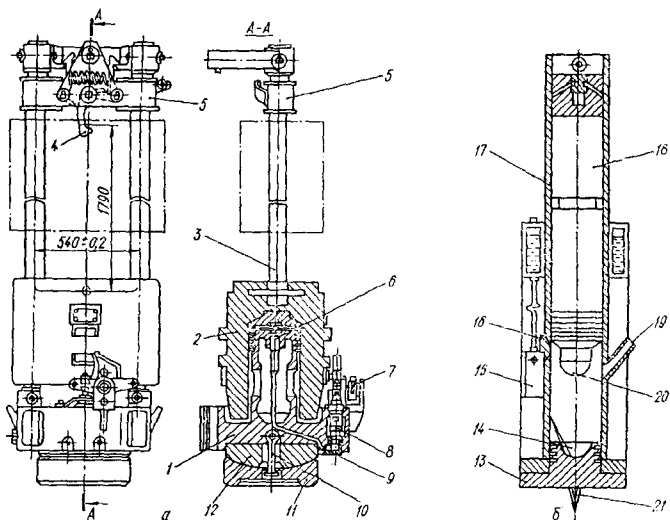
Дизельные молоты: а – штанговый; б – трубчатый; 1 – поршень; 2 – цилиндр; 3 – штанга; 4 – крюк; 5 – кошка; 6 – форсунка; 7 – толкатель; 8, 15 – топливные насосы; 9 – трубопровод; 10 – серьга; 11 – наголовник; 12 – сферическая плита; 13 – пята; 14 – углубление; 16 – рычажок; 17 – цилиндр; 18 – поршень; 19 – выхлопные окна; 20 – шаровая головка; 21 – штырь.
